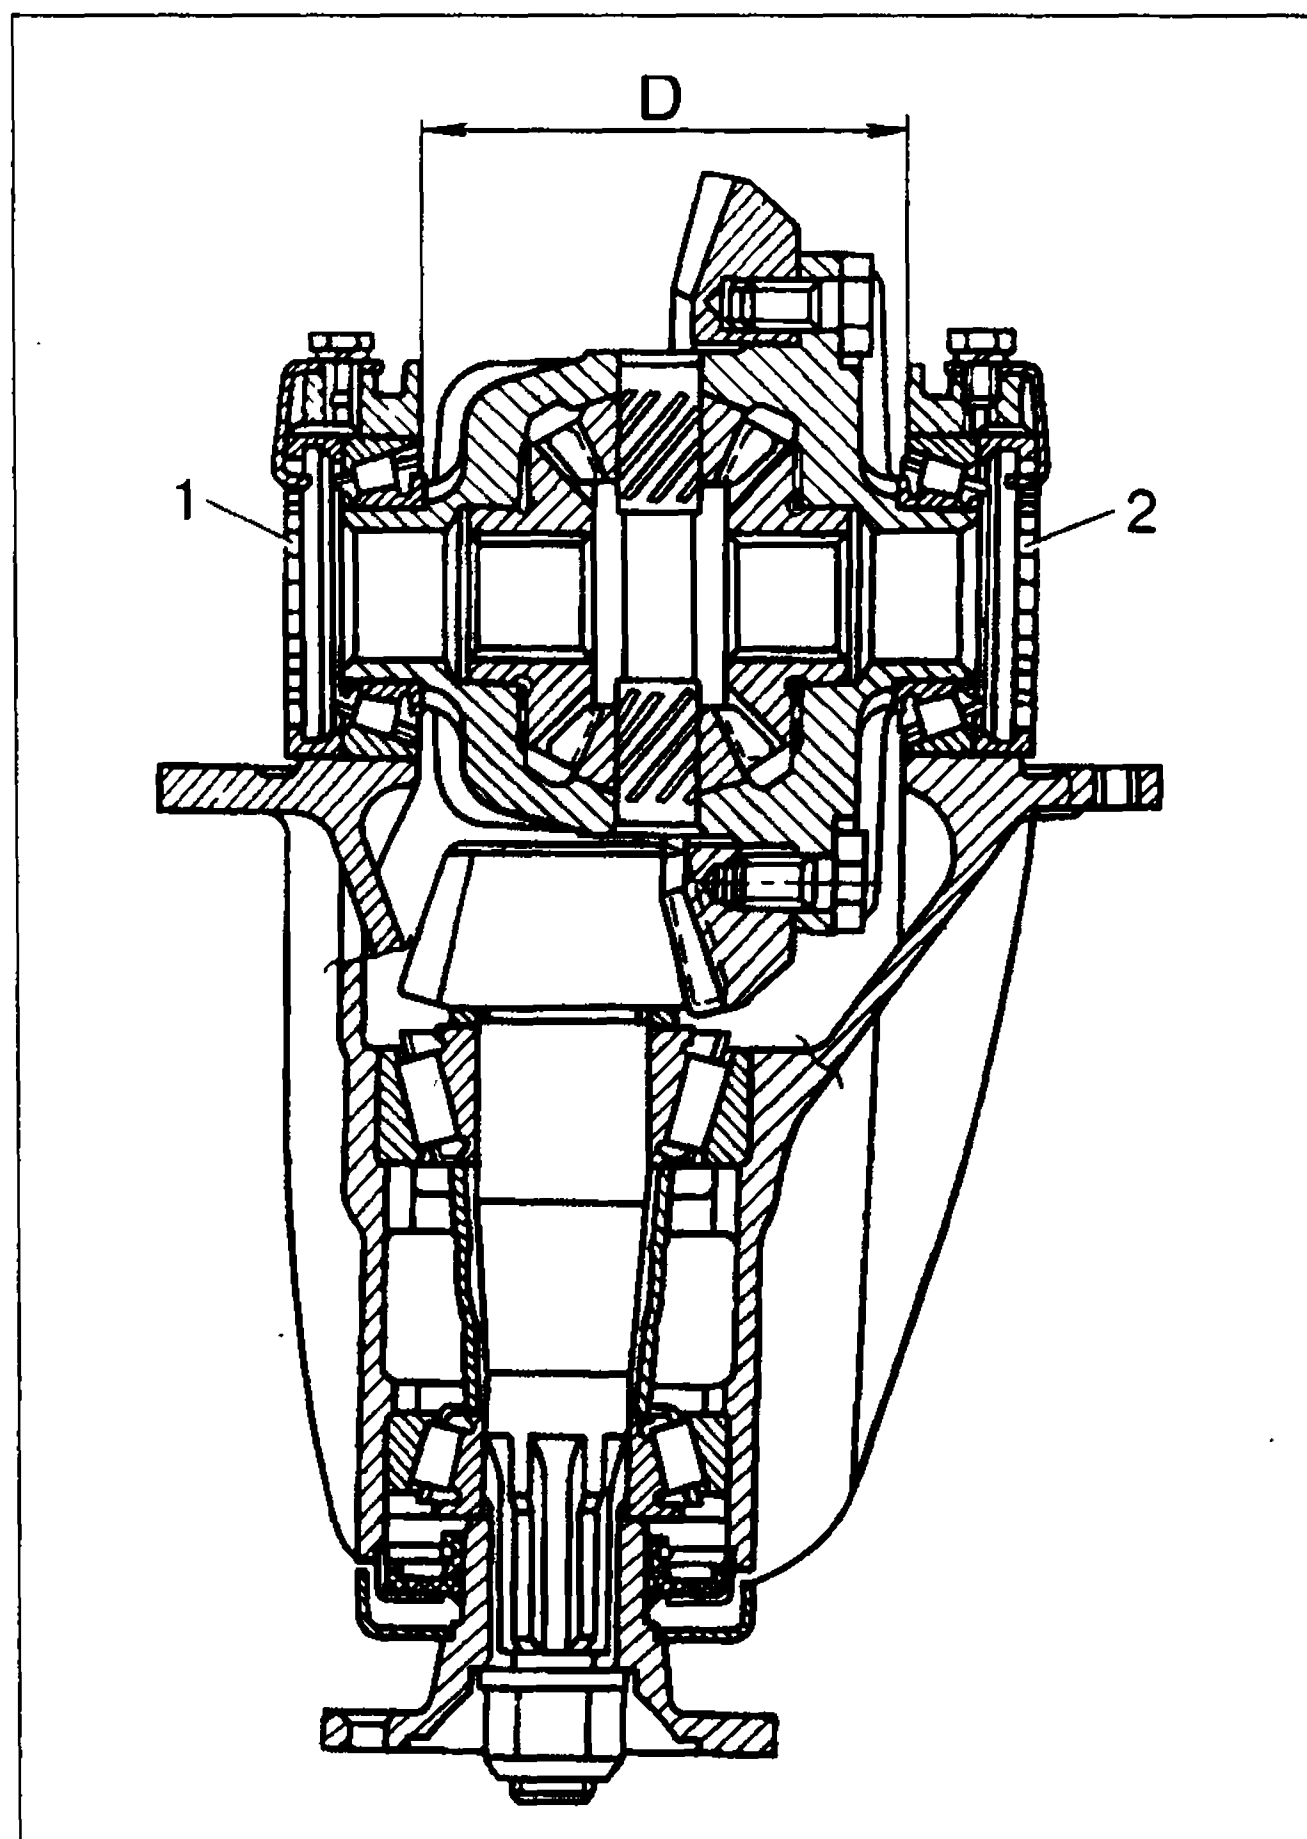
Схема проверки предварительного натяга подшипников коробки дифференциала:
